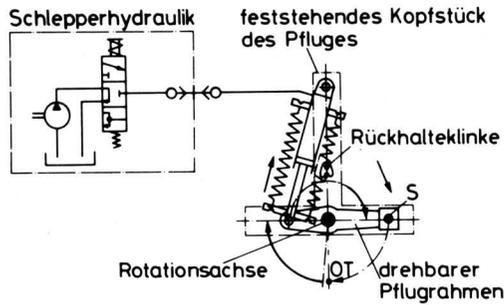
Hydraulisch unterstütztes Falldrehwerk.
